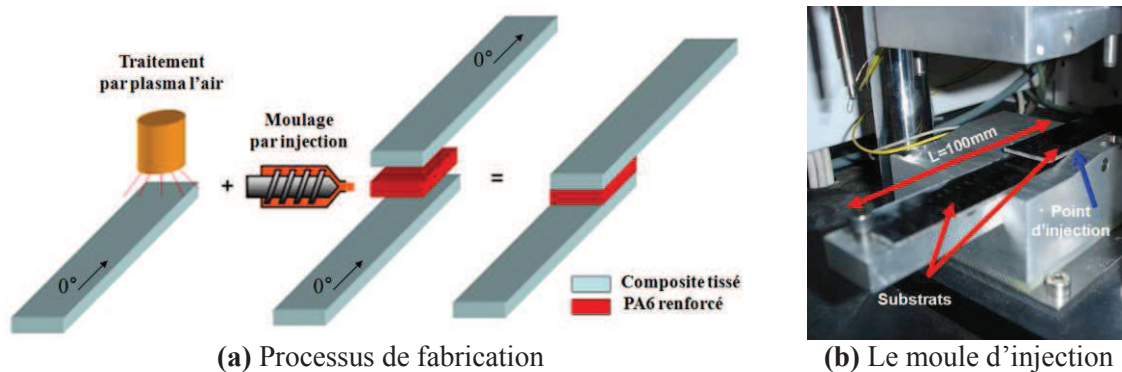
Processus de fabrication de l'éprouvette de simple recouvrement
